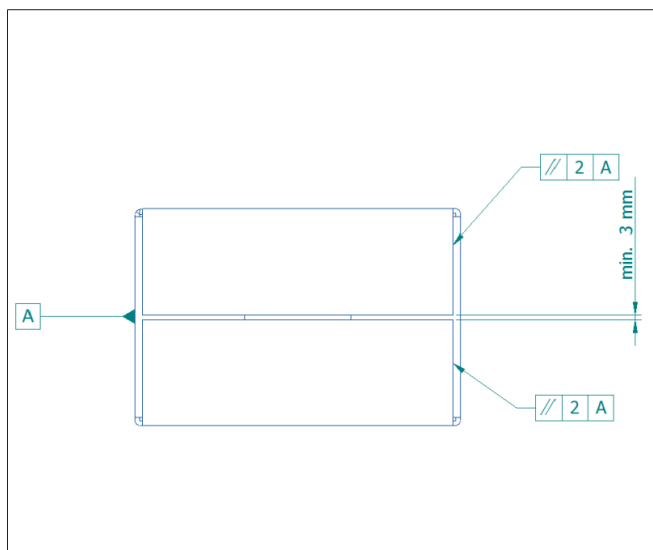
Картонная коробка с накладками крышки - допуски
